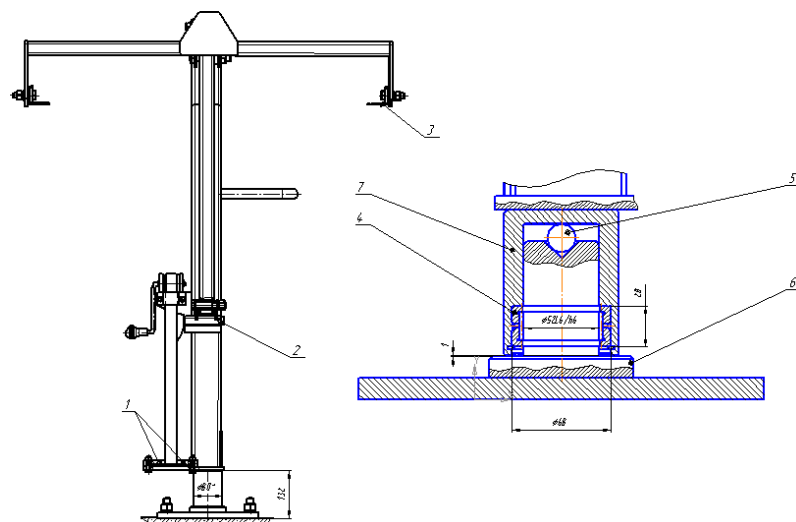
Поворотна стійка стенда для ремонту радіатора автомобіля
